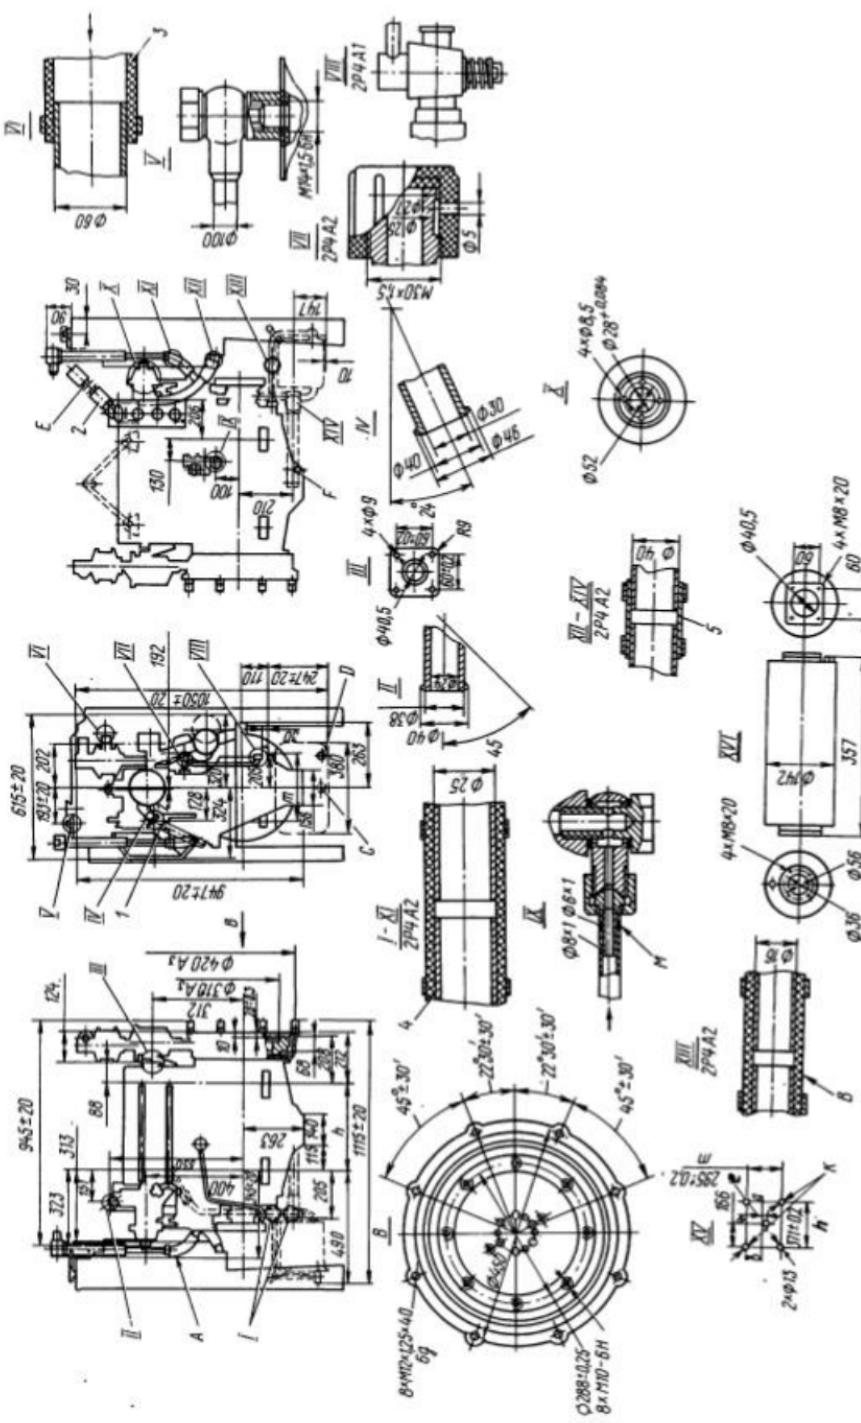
Габаритный чертеж дизеля 4Ч 8,5/11 (1Р4-6, 1Р4-7, 2Р4-6, 3Р4-6): А — кожух маховика и маховик (8 отв. М10×1,5 БН расположены равномерно по окружности с допуском ±0,02 мм); В — фланцы выпускного коллектора; I — патрубок водяного насоса; II — патрубок терmostата; III — подвод топлива из бака (S — место пайки); IV — патрубок подогревателя; V — воздушный вентилятор; VI — патрубок сливной охлаждающей жидкости из дизеля и присоединения подогревателя; VII — глушитель; VIII — расположение отверстий крепления днища (а — передний центральный; б — сзади); С — слив масла; D — слив охлаждающей жидкости
